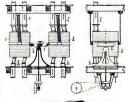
v. 15. Plansichter von der Braunschweigischen üntenbuugnstatt Amme, Giesecke & Konegen, Braunschweig.
